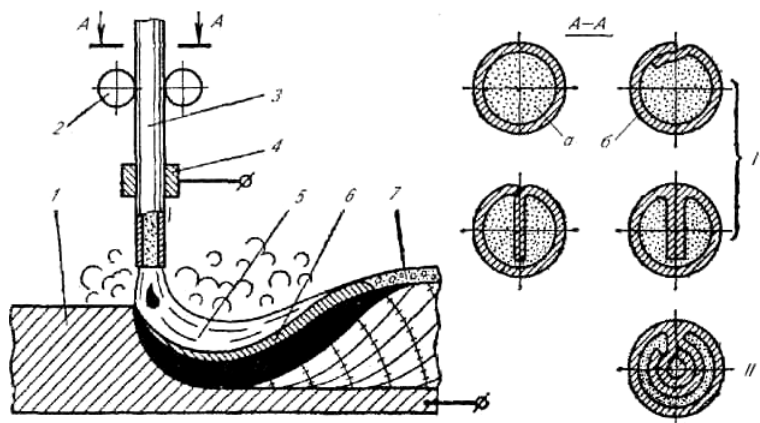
Автоматическая сварка порошковой проволокой
